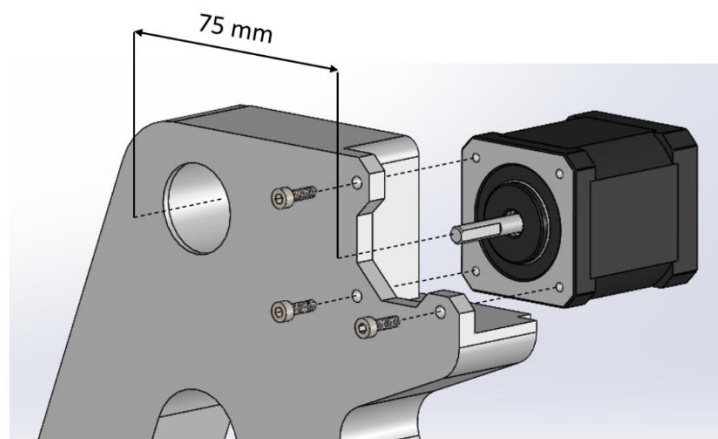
Montagem do Motor de passo ao Suporte angular
